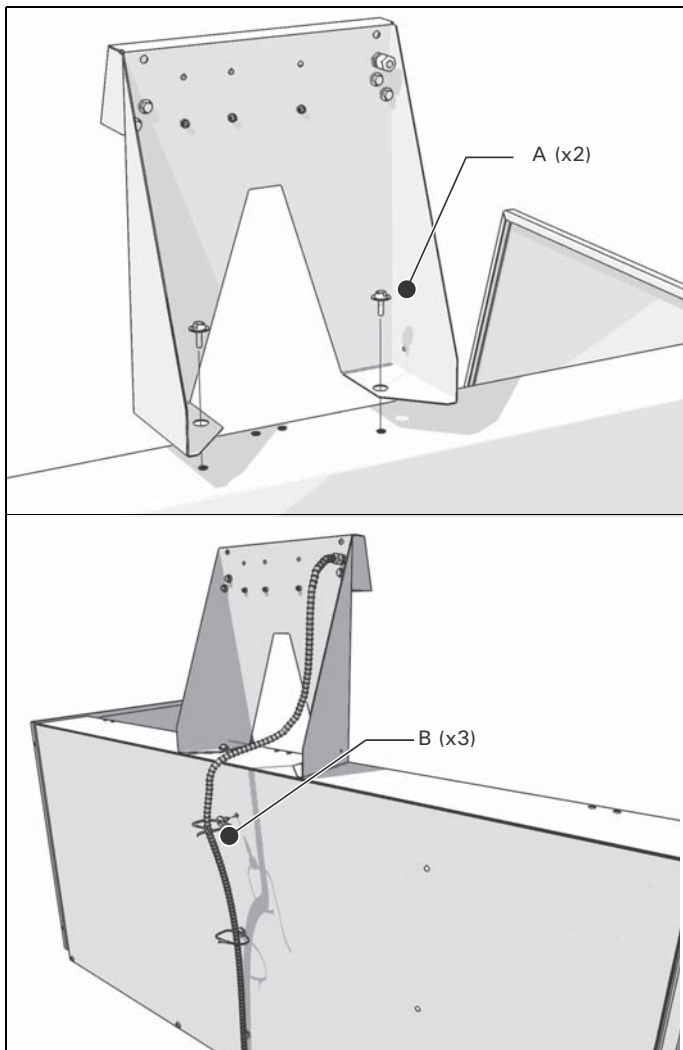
Montage des Bewegungssensors (Rückansicht)
